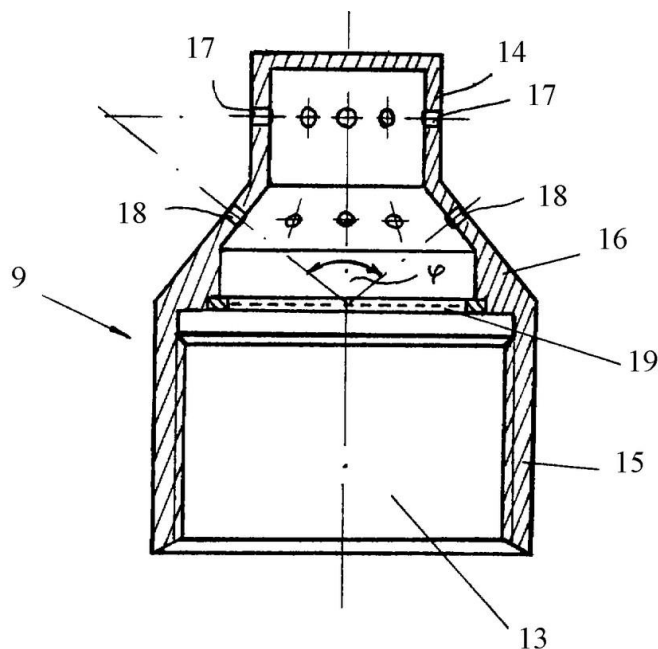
Схема распылительной насадки (продольный разрез)
